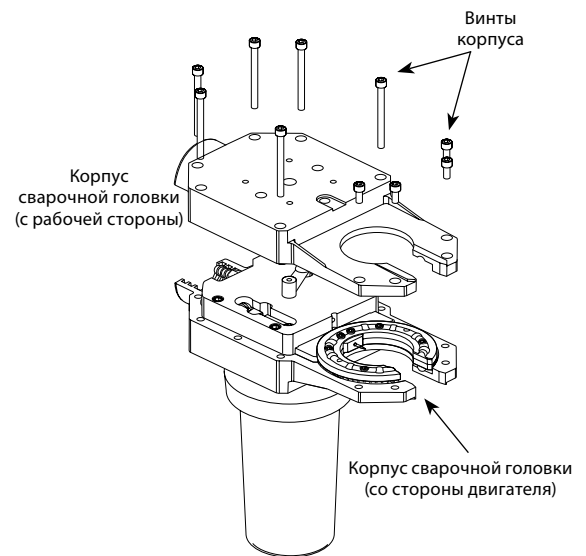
Снятие половины корпуса сварочной головки со стопорным кольцом
